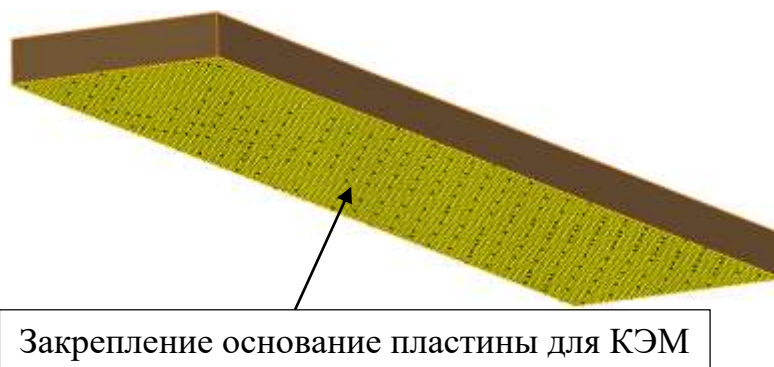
Схема закрепления детали в процессе обработки
